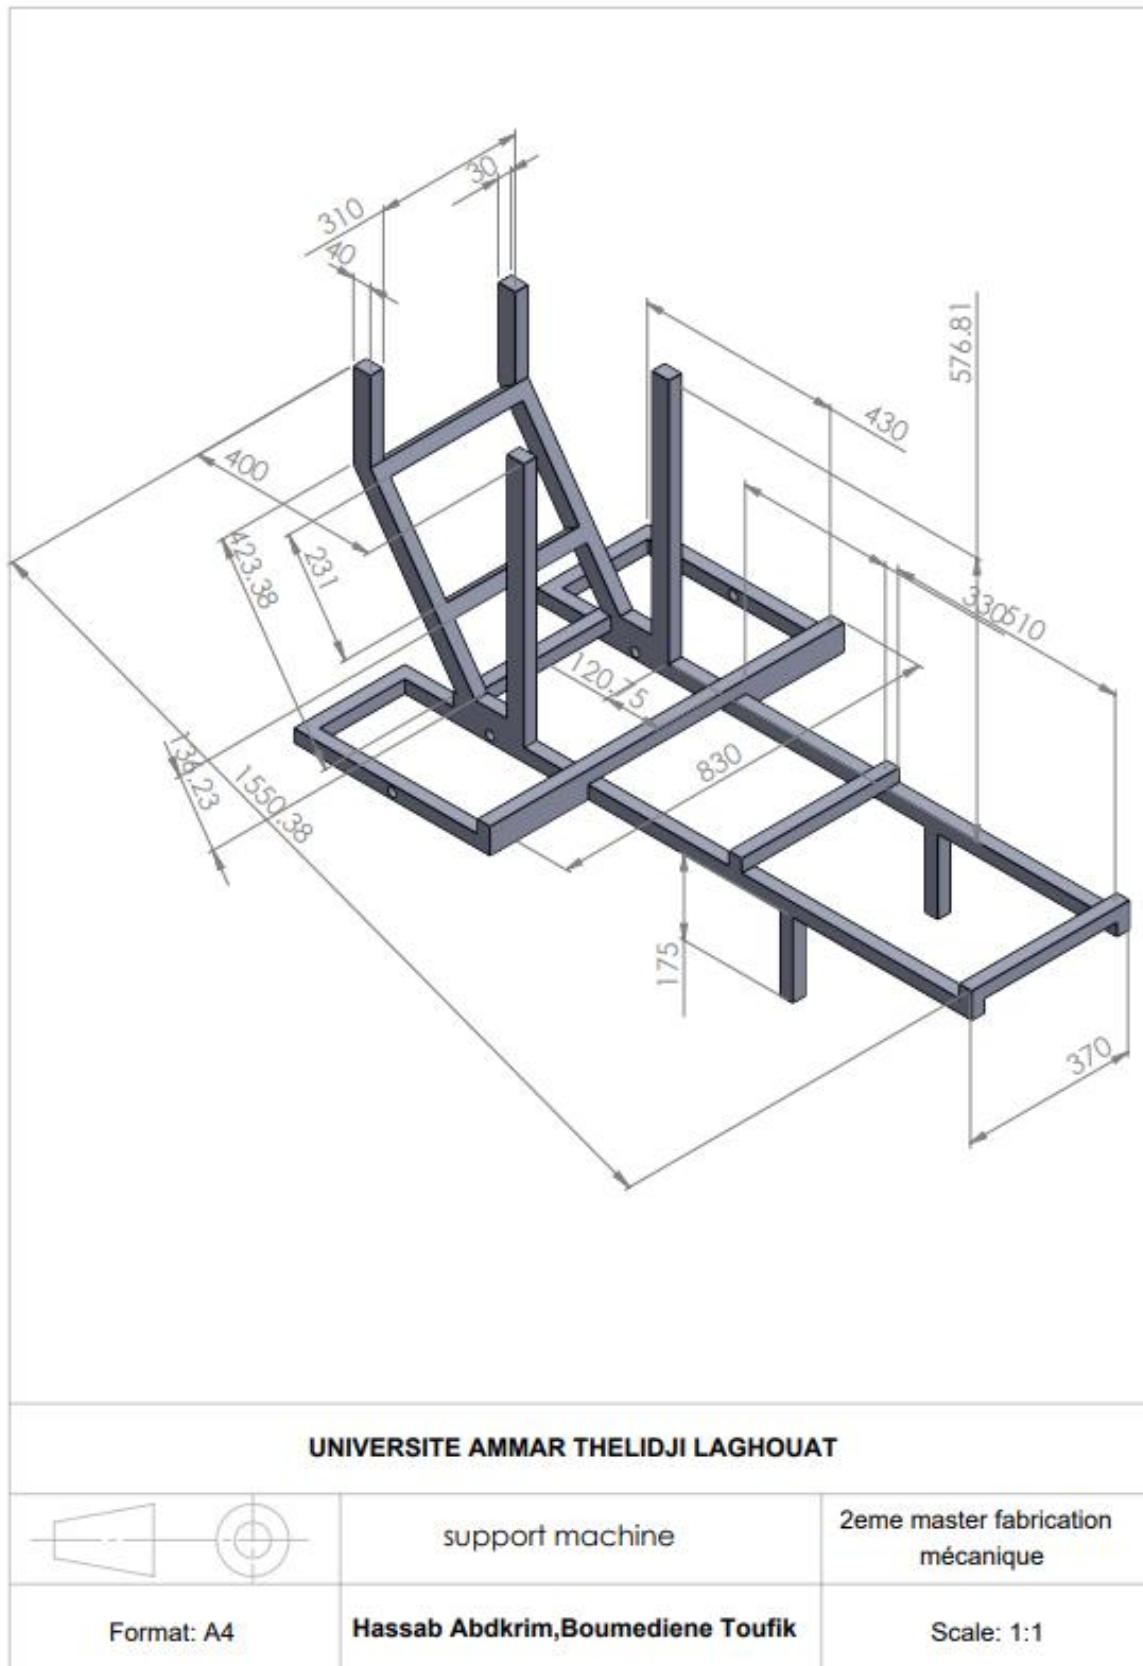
Dessin technique de support machine de la nouvelle conception
